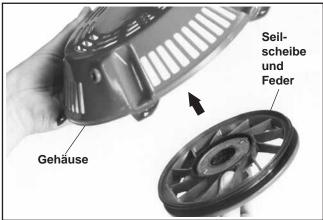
Seilscheibe und Feder im Gehäuse anbringen.
